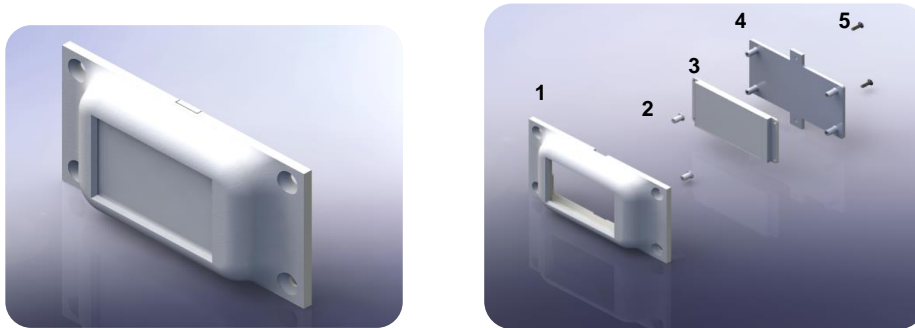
Ensamblaje - Explosionado, modelo tentativo cubierta frontal. Fuente: Autor
